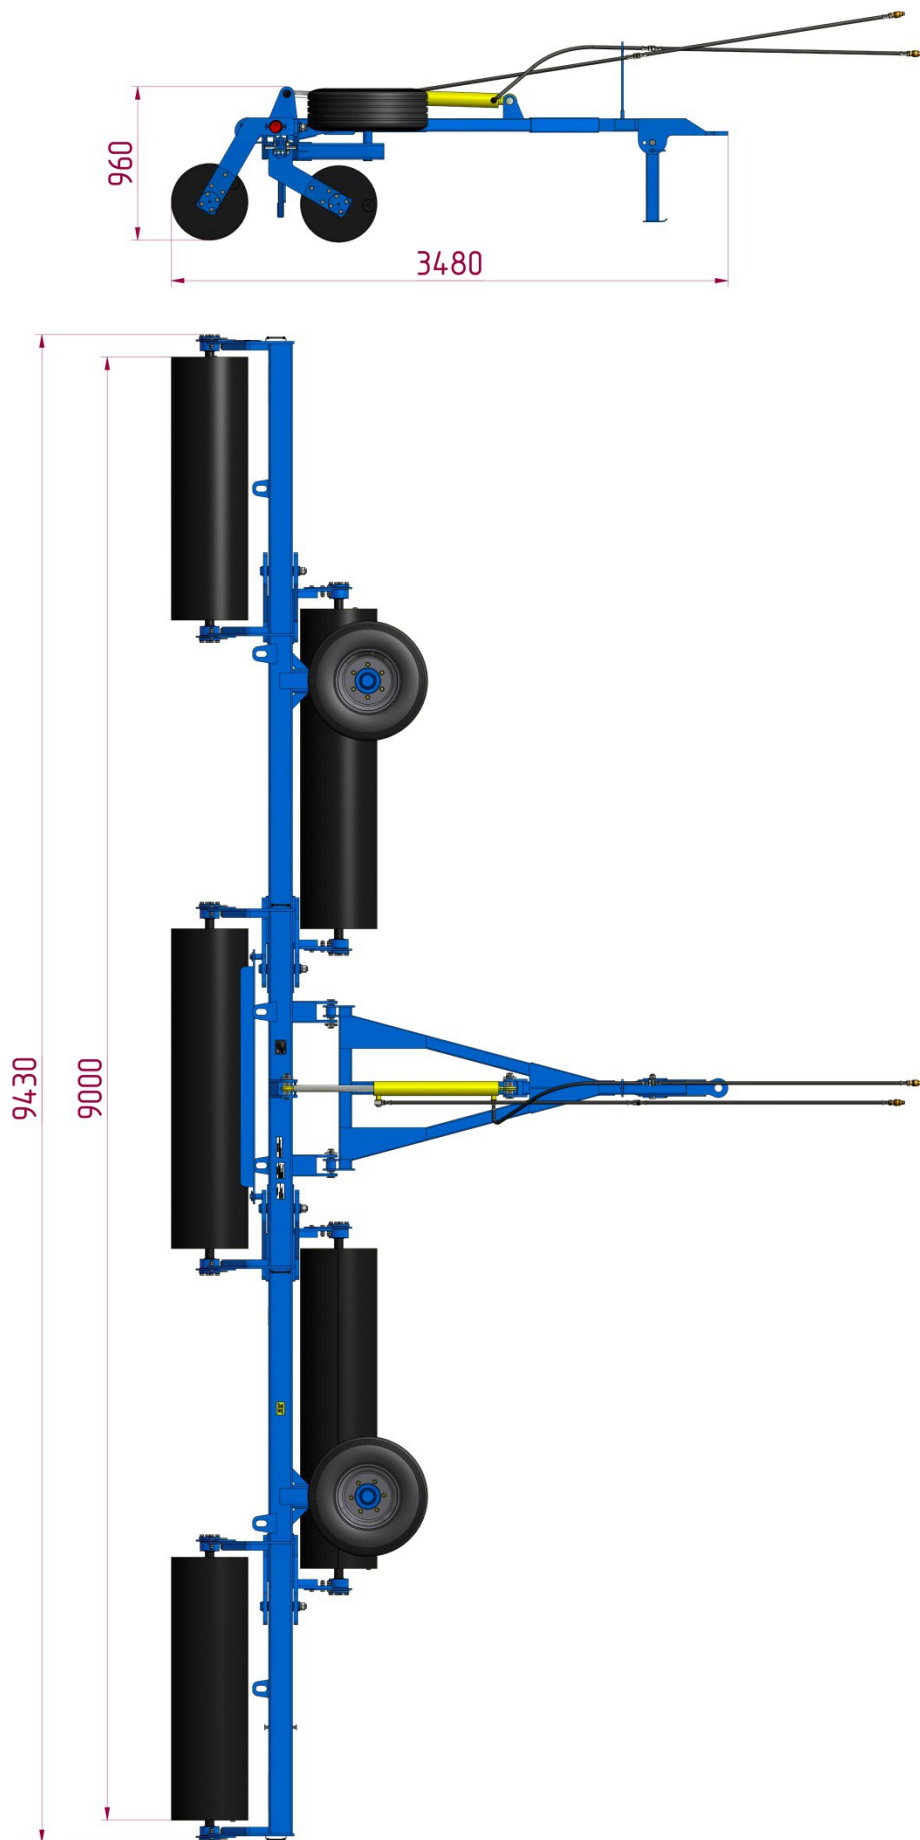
в. Габаритные размеры в рабочем положении КВНГ-9.2Н
